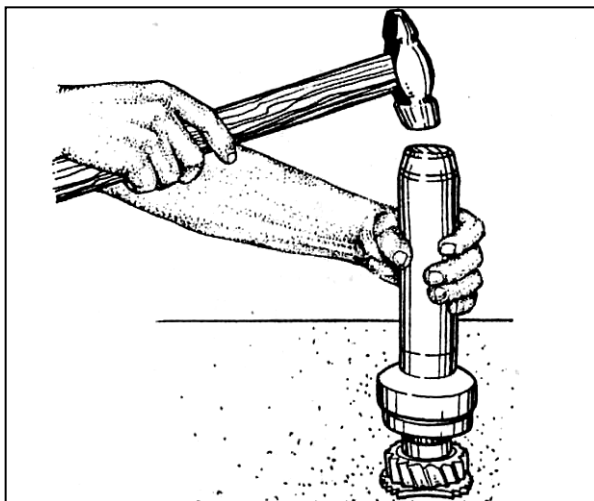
Напресування кулькового підшипника на первинний вал
